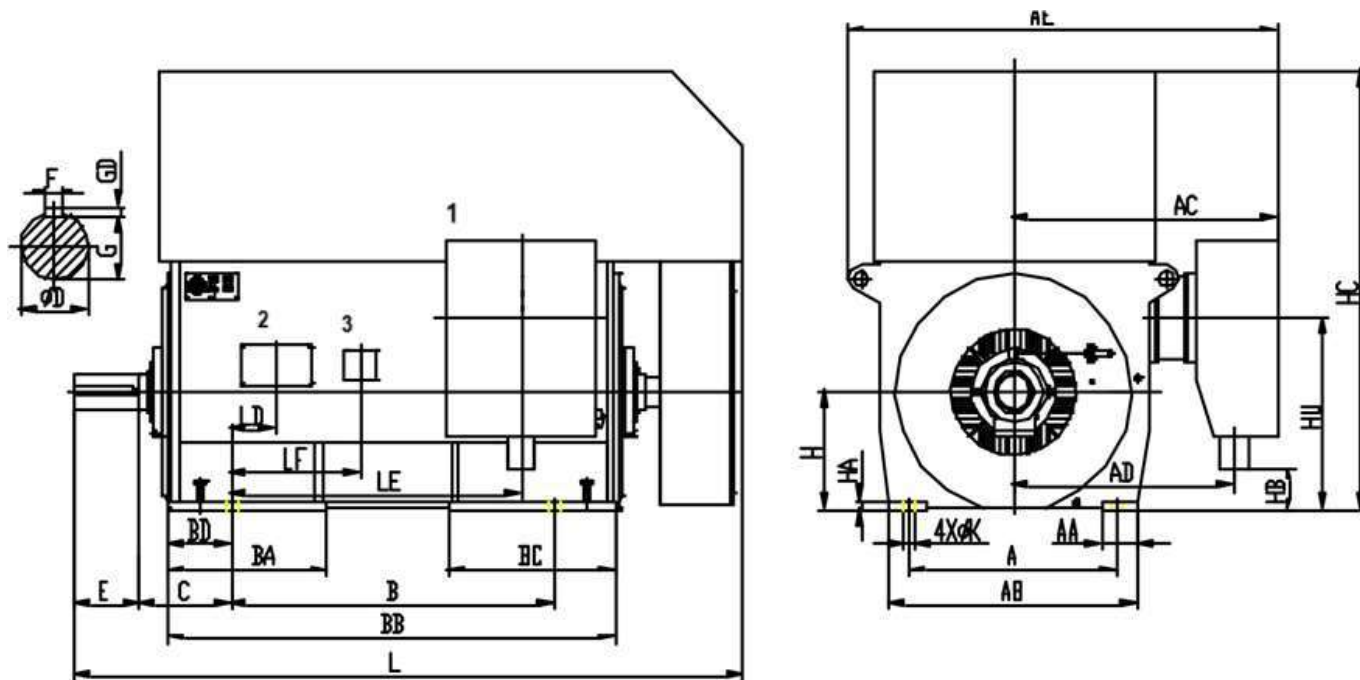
Установочные размеры двигателей серии YZYKK (поз.1 – главная коробка выводов, поз.2 – коробка выводов термодатчиков, поз.3 - коробка выводов обогревателя)
